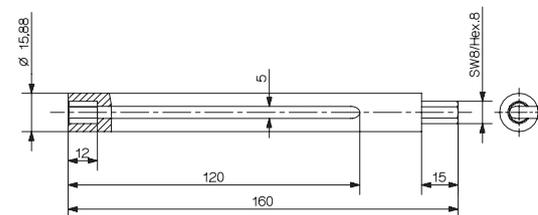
Montageschlüssel für tiefe Bohrungen Typ 1300A41
